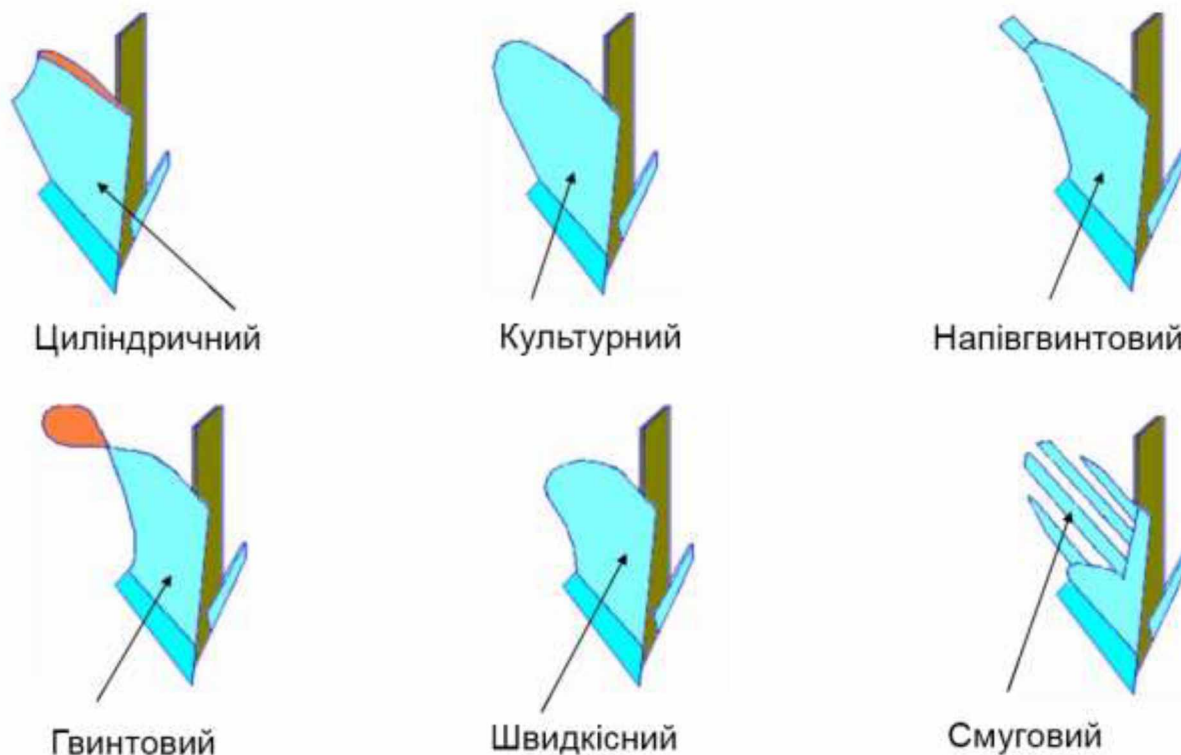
Типи плужних робочих корпусів для відвальної оранки
